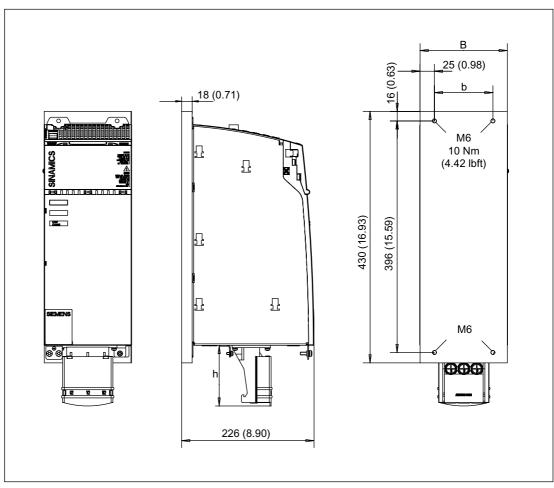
Disegno quotato Motor Module con Cold-Plate 60 A e 85 A
